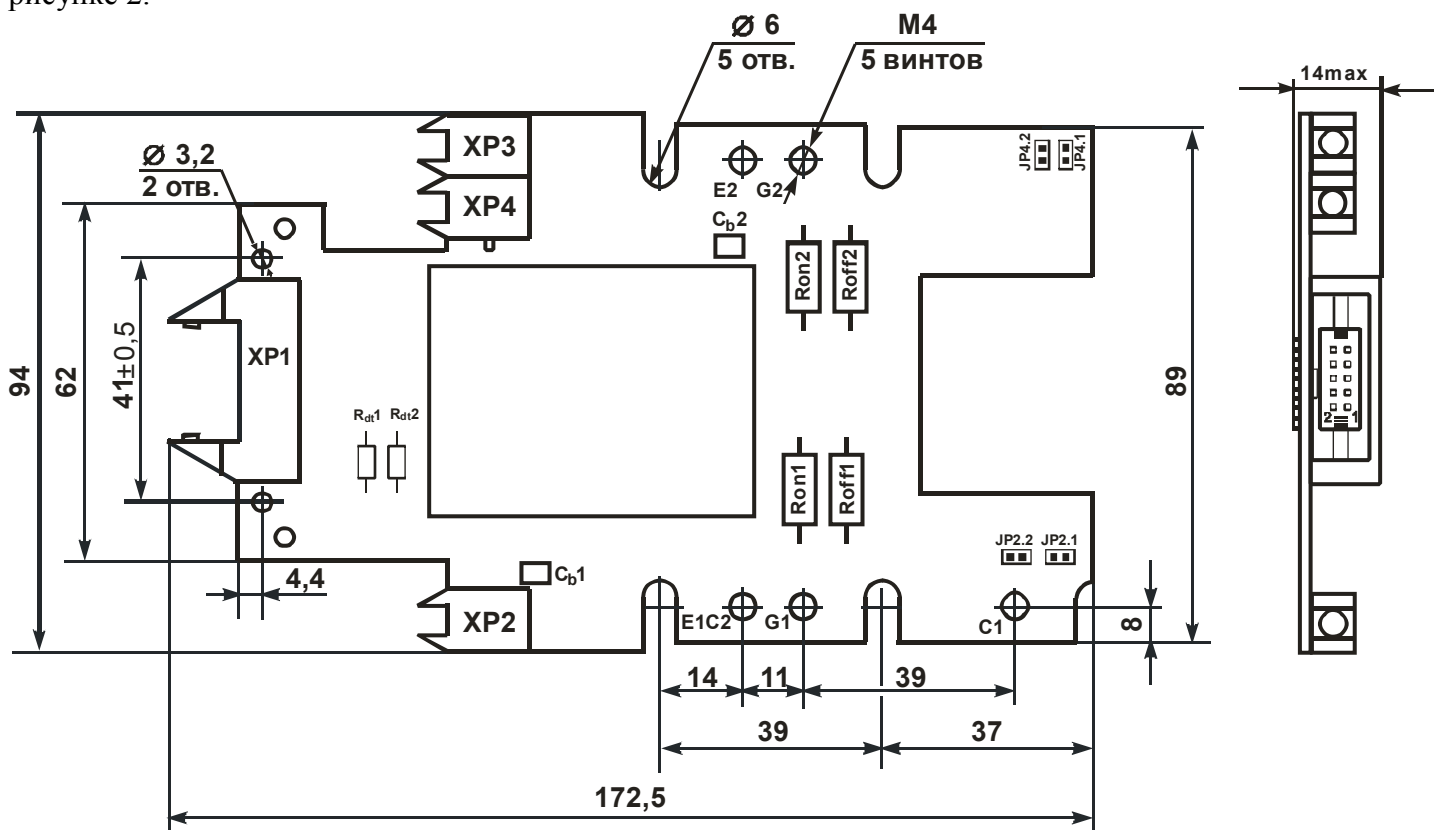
Габаритный чертёж драйвера ДР2180П-БВ1-1
